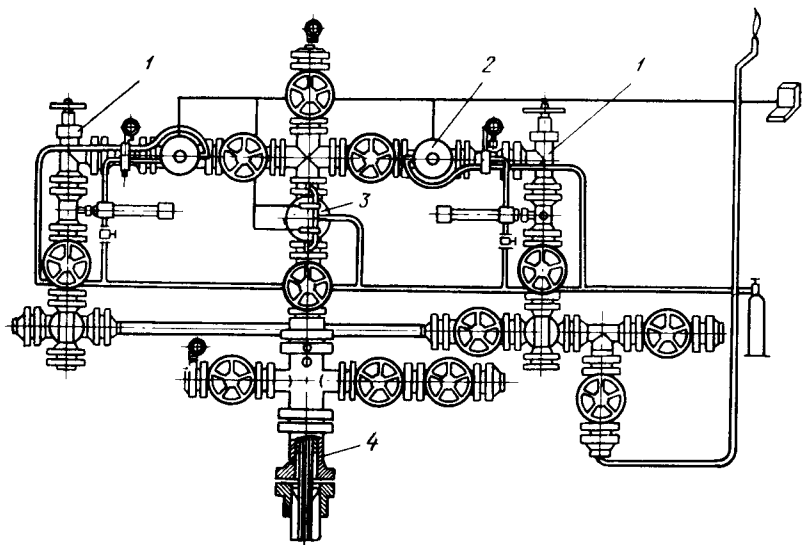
Комплекс устьевого оборудования для высокодебитных скважин: 1 — угловой регулирующий штуцер; 2 — автоматический отсекающий; 3 — стволовая пневматическая задвижка; 4 — трубная головка
